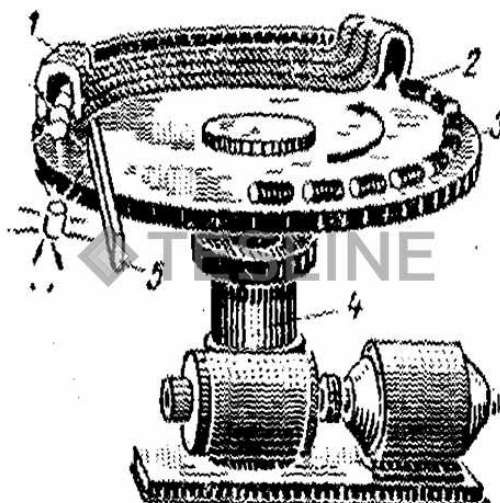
Схема карусельного нагревателя с щелевым индуктором:
